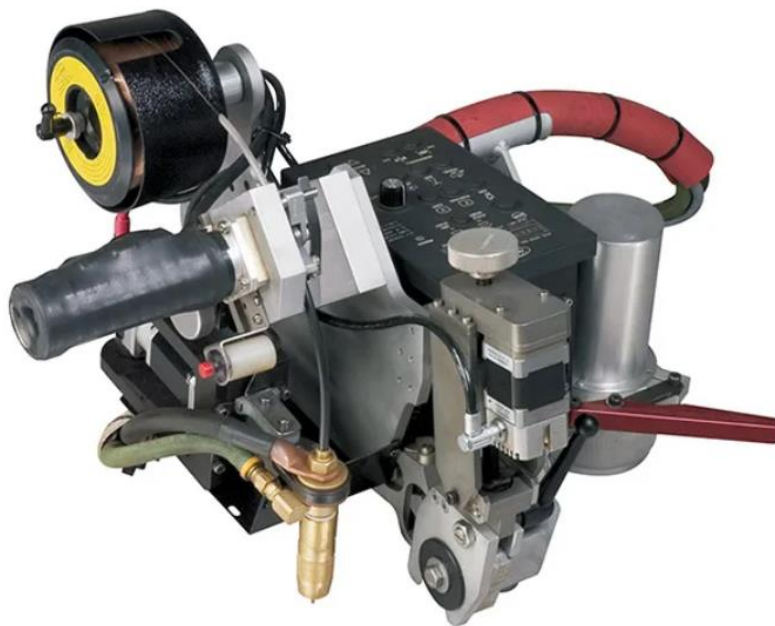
Сварочная головка «П-260» («P-260»)
